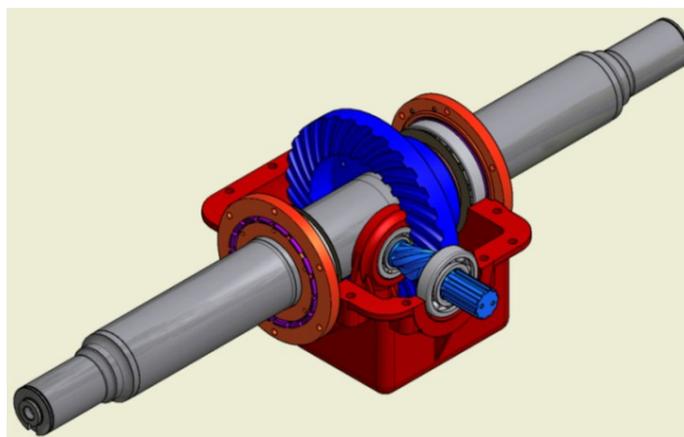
Колёсный редуктор с ExSyGear зацеплением для локомотива МПТ6 (изделие 1)
